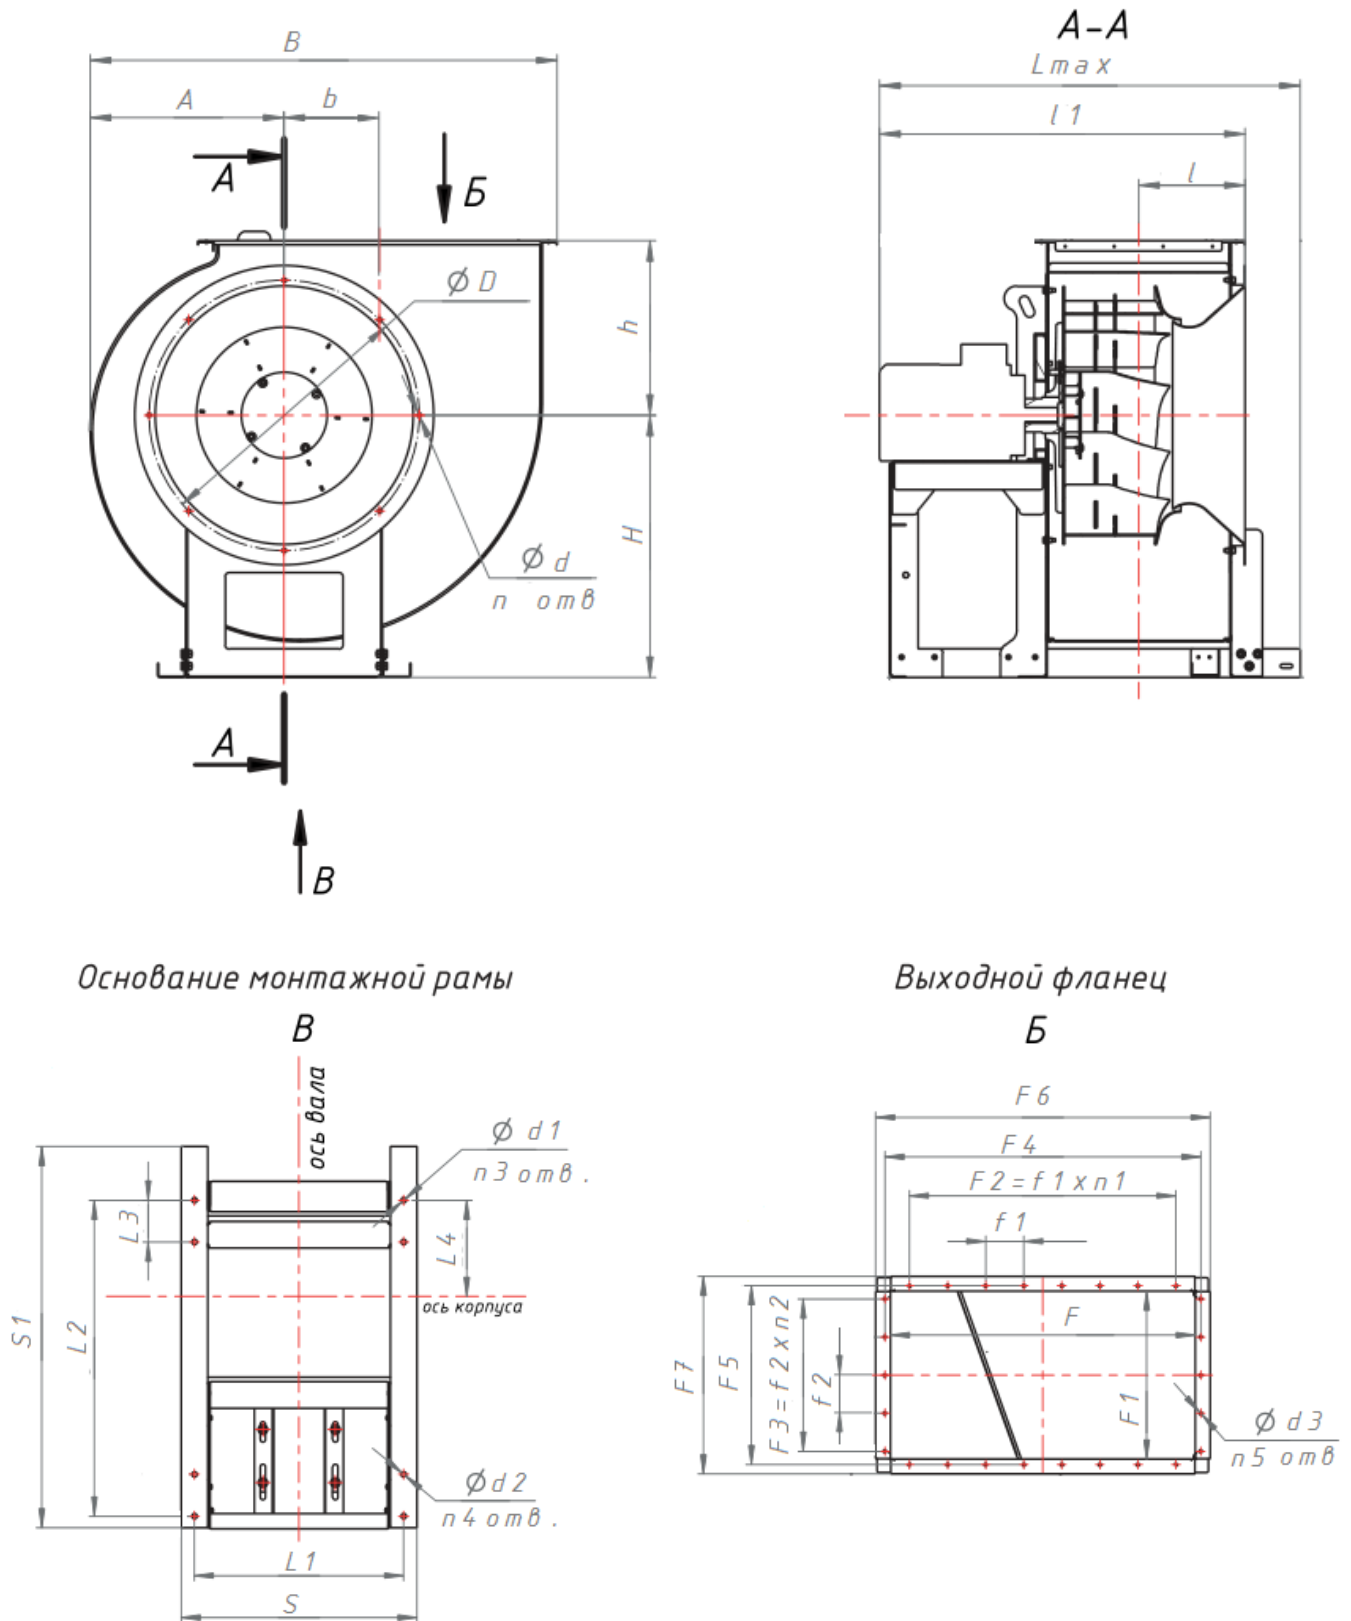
Габаритные, присоединительные размеры и общий вид вентиляторов RAD-ДУ
